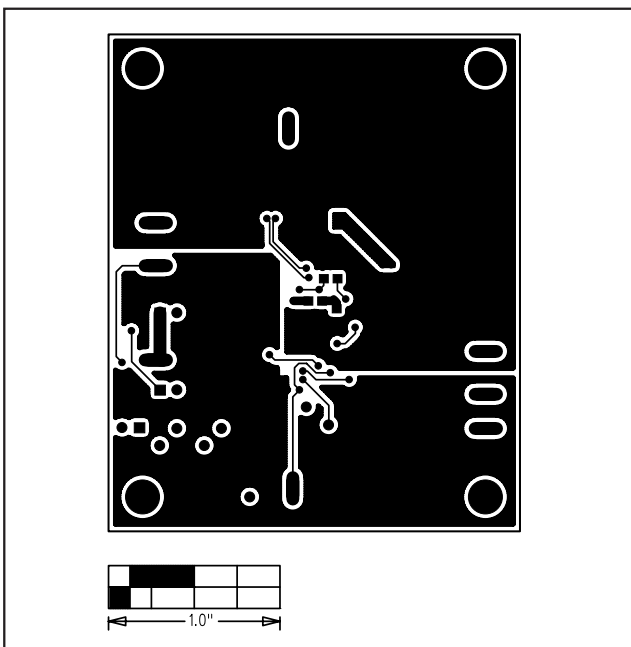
MAX1870A 评估板 PCB 布局图 — 焊接面
